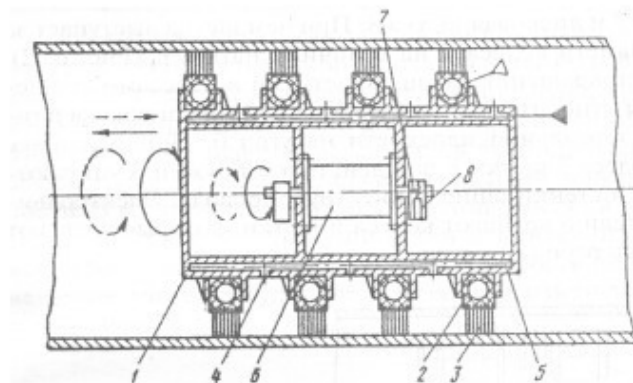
Очистное устройство с реверсивным поступательным движением, где 1 – корпус; 2 – эластичный рукав; 3 – щетка; 4 – сопла; 5 – каналы; 6 – двигатель; 7, 8 – дебалансы.
